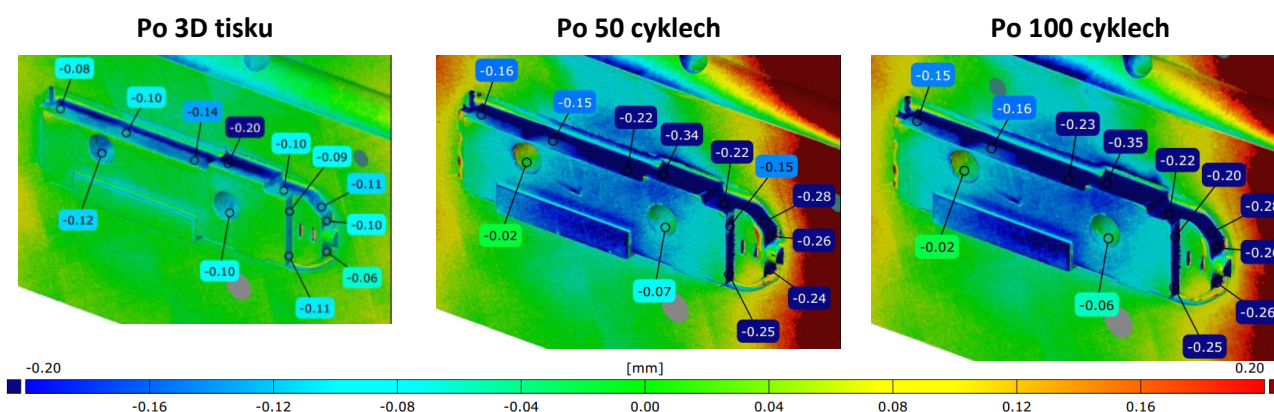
Pohyblivá vložka – Strana v dělicí rovině – Výstupek krytu se zkratkou RTI – detail 1
